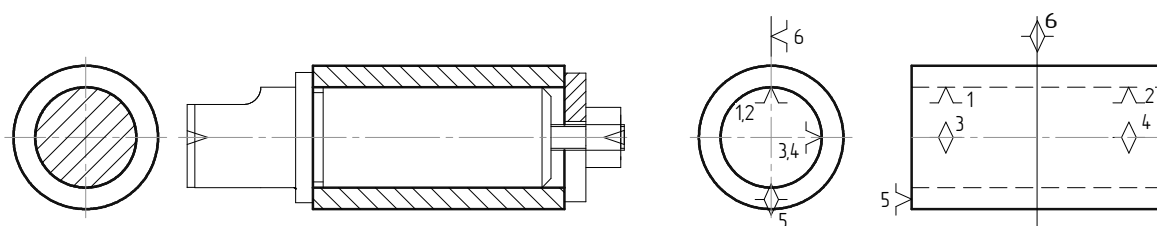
Схема базування втулки на циліндричній оправці з зазором.
